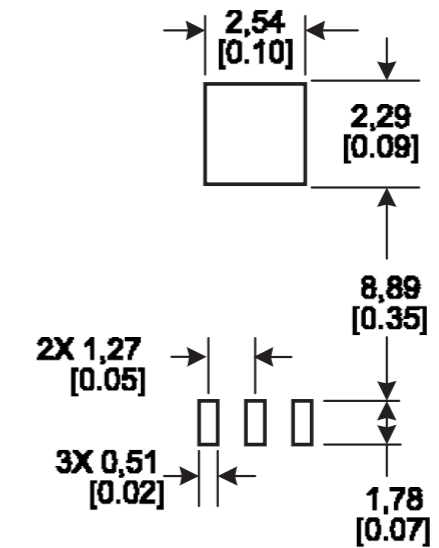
HIH-5031 PCB 焊盘 (仅供参考 mm/[in])
